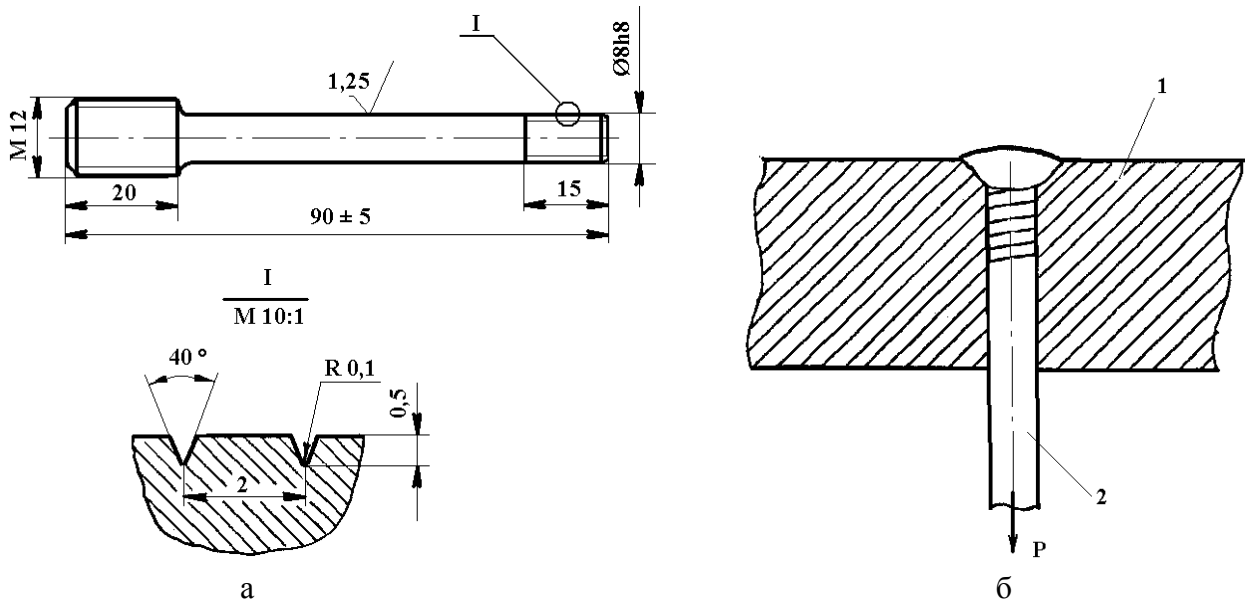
Образец-вставка сварного соединения для испытания по методу «Имплант»: а – образец-вставка; б – образец сварного соединения с опорной плитой I
